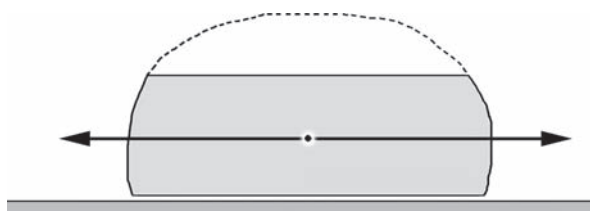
Форма заготовки после обработки на абразивной плоскости.
